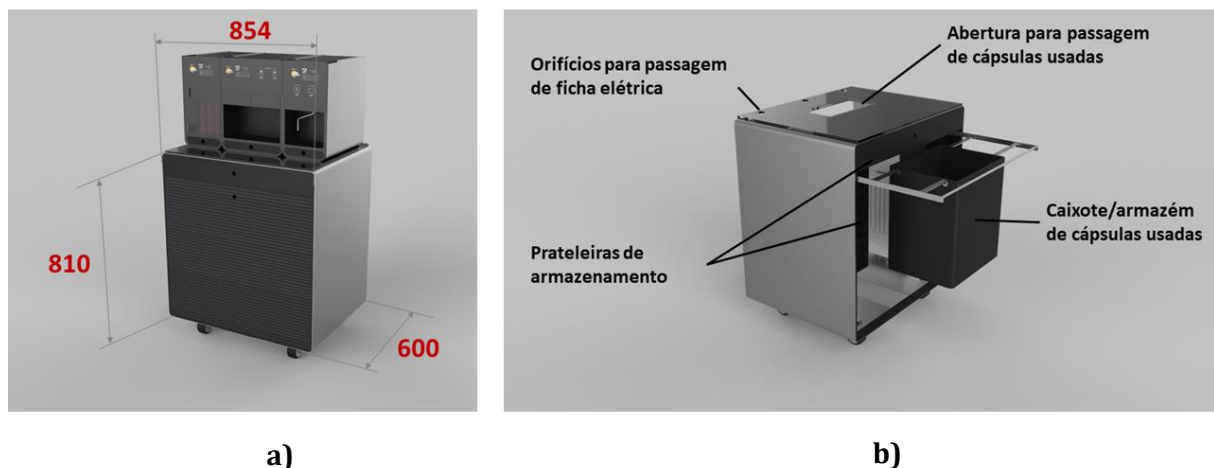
Modelação do carrinho em *SolidWorks*® [60] – adaptado de [79]: a) conjunto do carrinho com a máquina e com indicação das dimensões do mesmo; b) carrinho com identificação de alguns dos seus principais detalhes.
